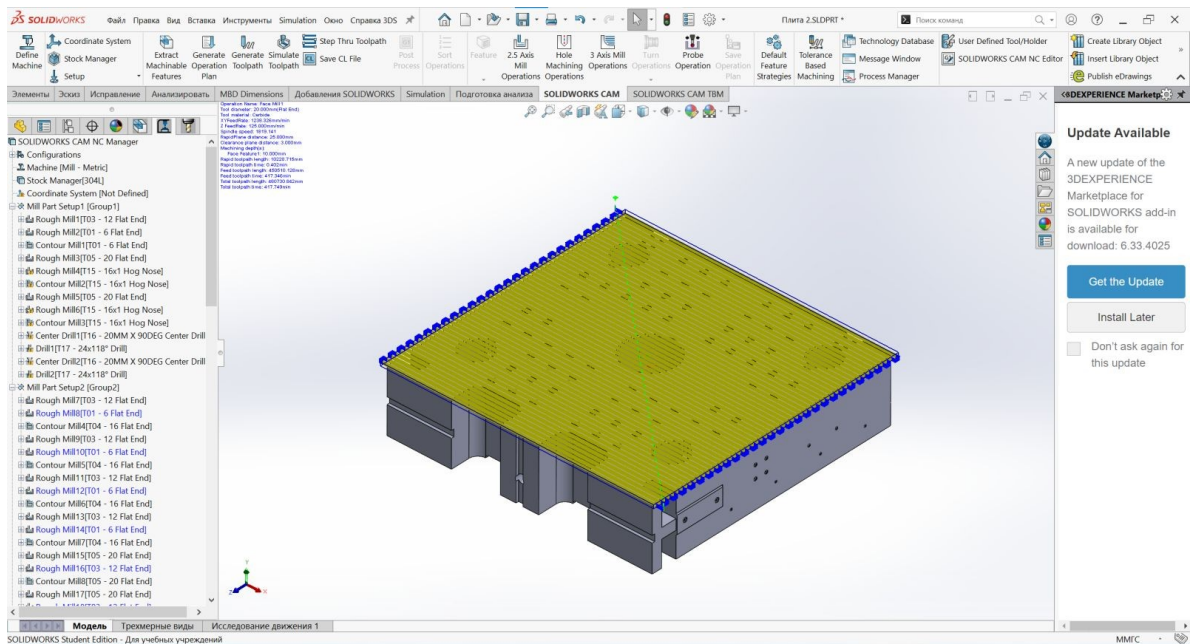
Траекторія руху інструменту при фрезеруванні площини
